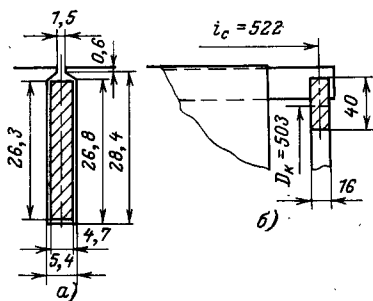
Паз ротора и соединение стержня с кольцом глубокопазного двигателя типа А114-8.
